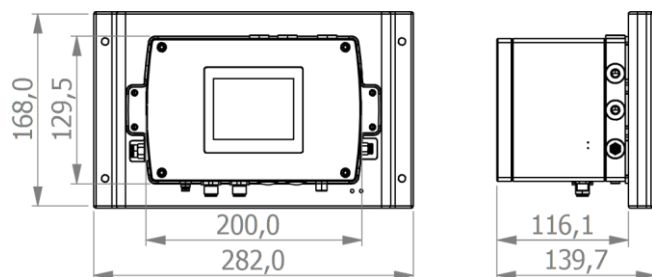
OIL CHECK 500 de Dimensions | Modèle fixe
